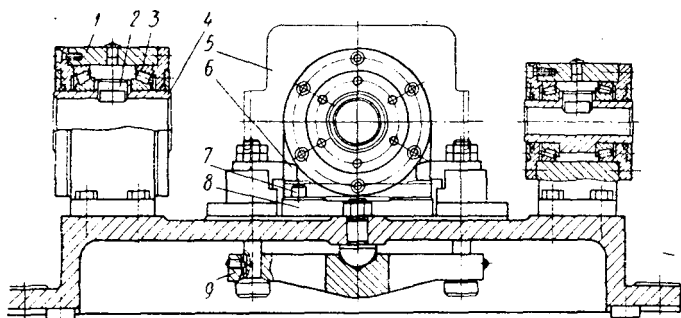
Приспособление к расточным станкам с ручным закреплением обрабатываемой детали
